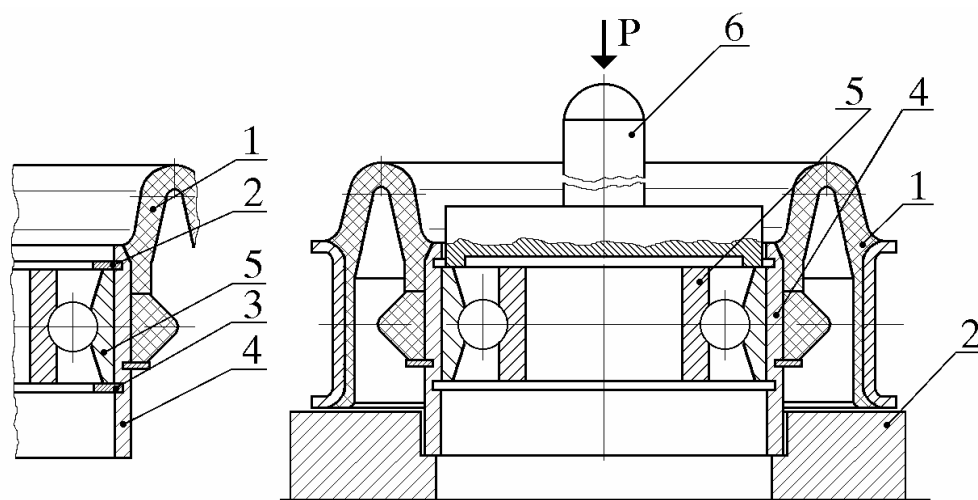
Выпрессовка шарикового подшипника из корпуса промежуточной опоры: 1 - опора промежуточная; 2 - приспособление; 3 - кольцо стопорное; 4 - корпус подшипника; 5 - подшипник шариковый; 6 - оправка технологическая
